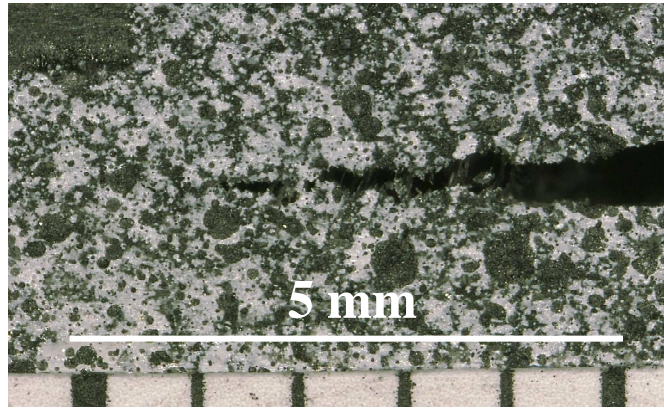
Ouverture de l'assemblage, juste avant la rupture finale.
